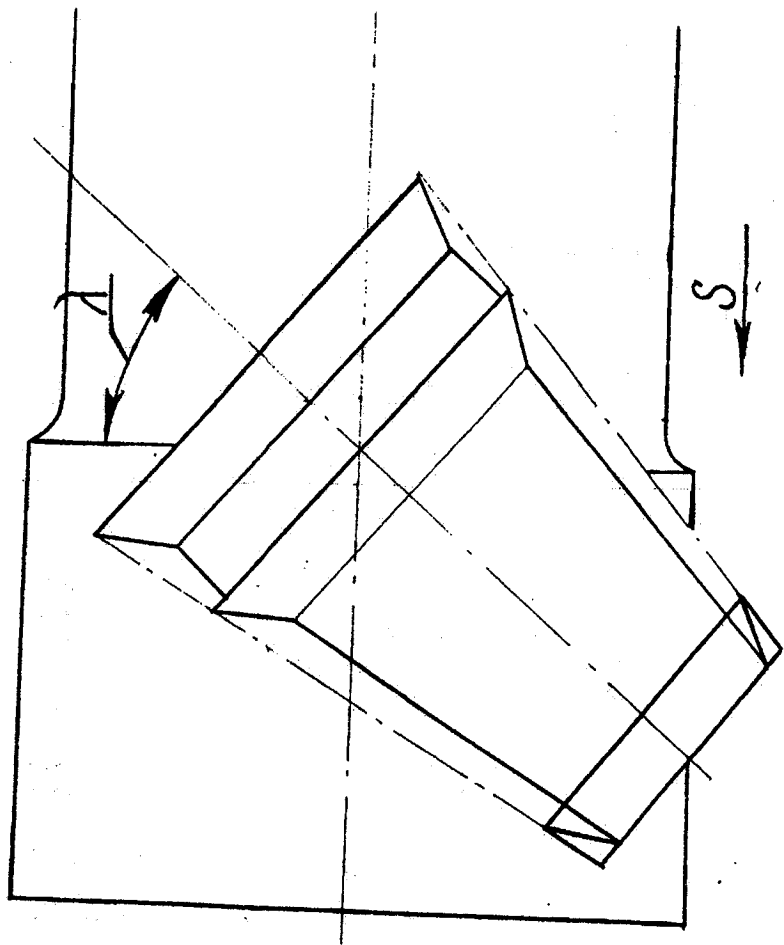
Схема різця з блока ріжучих кромки
